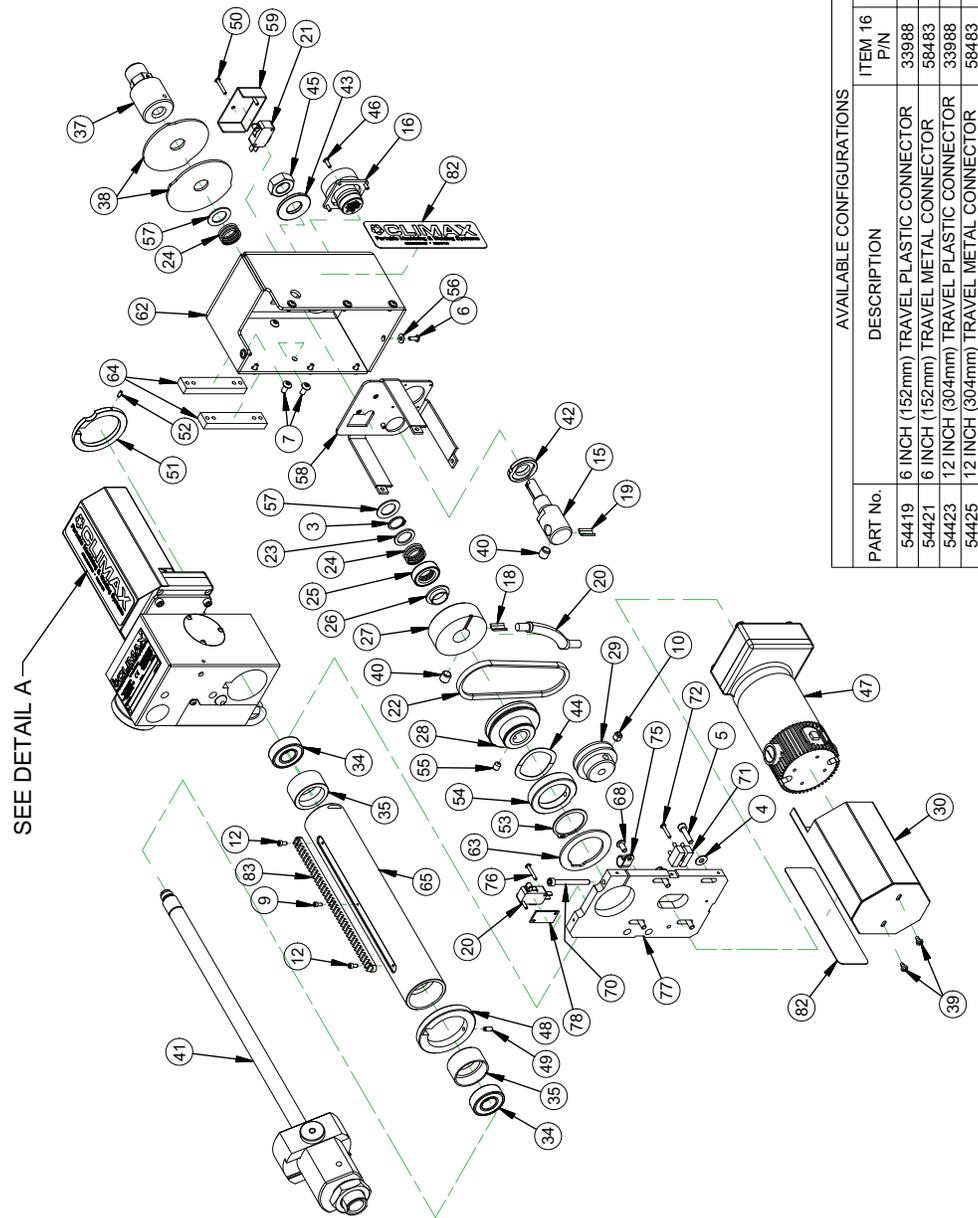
BW3000 LISTE DES PIÈCES DE L'ENSEMBLE 1 (RÉF. 103159)
